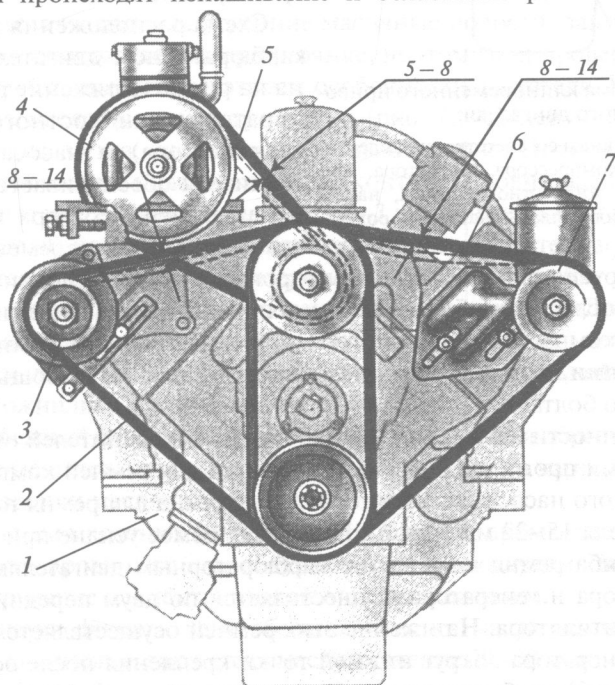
Схема проверки натяжения приводных ремней агрегатов двигателя: 1 – двигатель; 2, 5, 6 – ремни соответственно привода генератора, компрессора и гидроусилителя; 3, 4, 7 – шкивы соответственно генератора, компрессора и гидроусилителя
